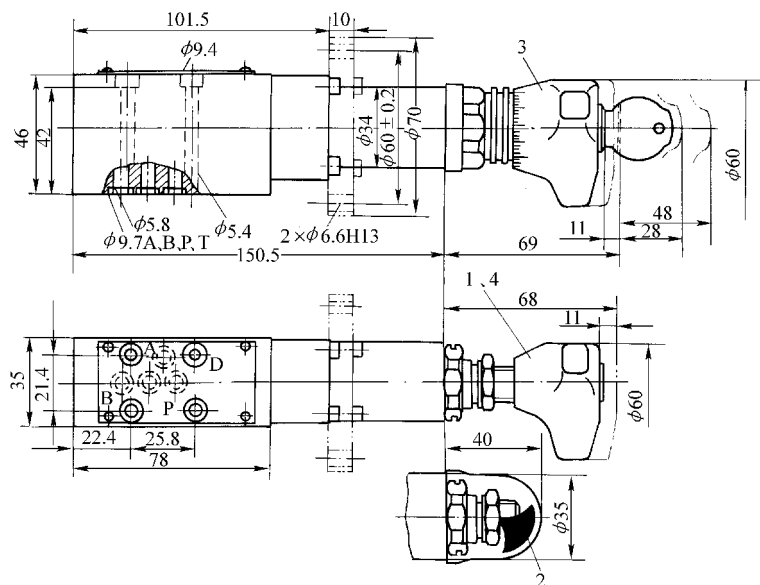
DZ5DP 型直动式顺序阀外形尺寸
